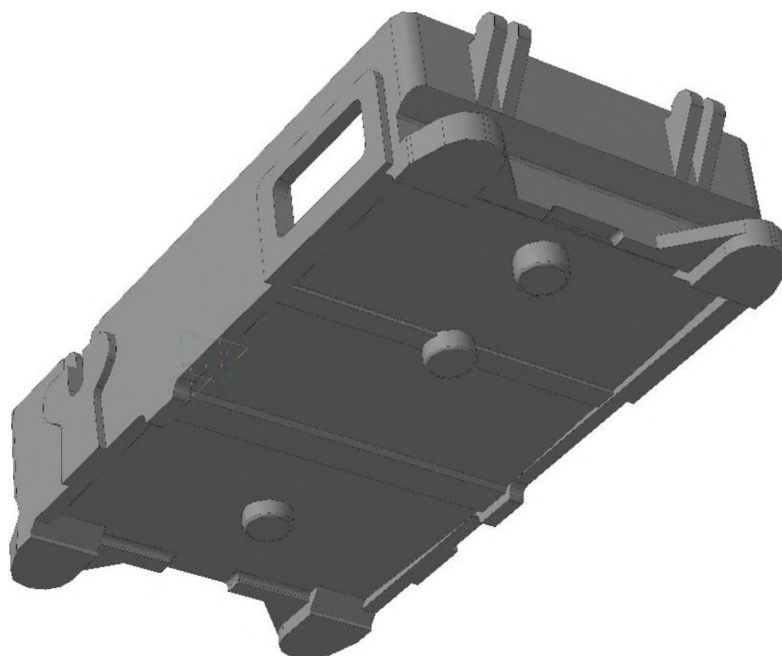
3D модель деталі «Корпус». Ізометрія, вигляд знизу
